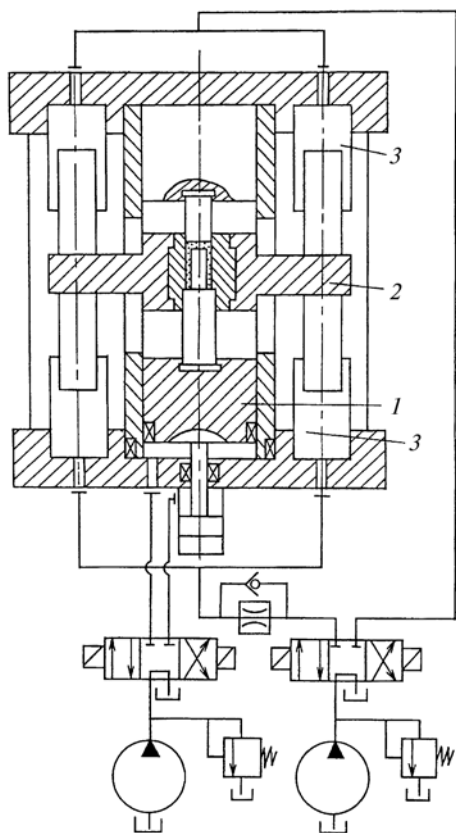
Конструкция пресса для формирования порошков со сдвигами частиц
